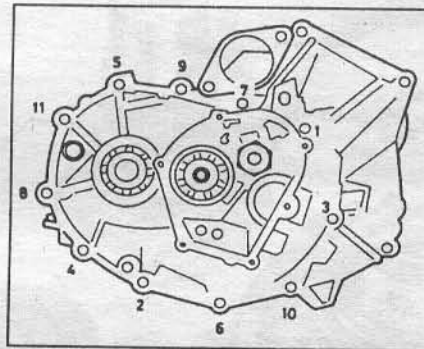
Порядок затяжки болтов крепления коробки к картеру.
